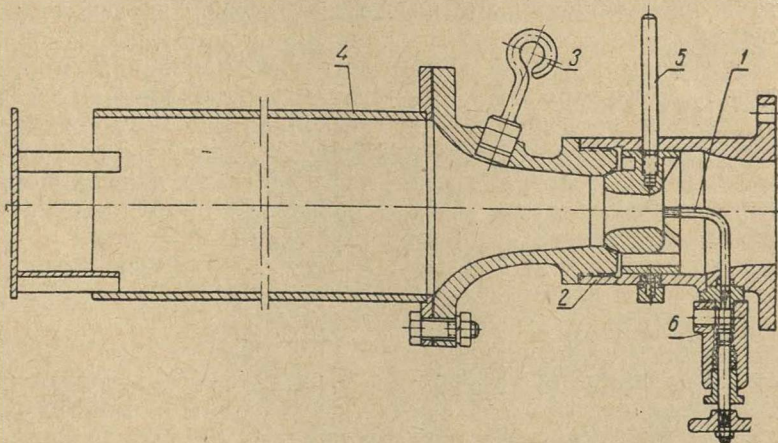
Схема горелки приспособления ПНГ—ВИЭСХ: 1—топливная трубка; 2—корпус; 3—пробка запального отверстия; 4—камера; 5—рукоятка для регулирования подачи воздуха; 6—топливный вентиль.
